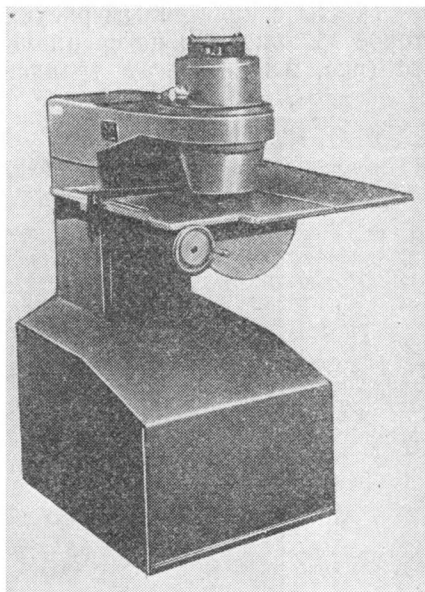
Дисковые ножницы для резки материала на заготовки
